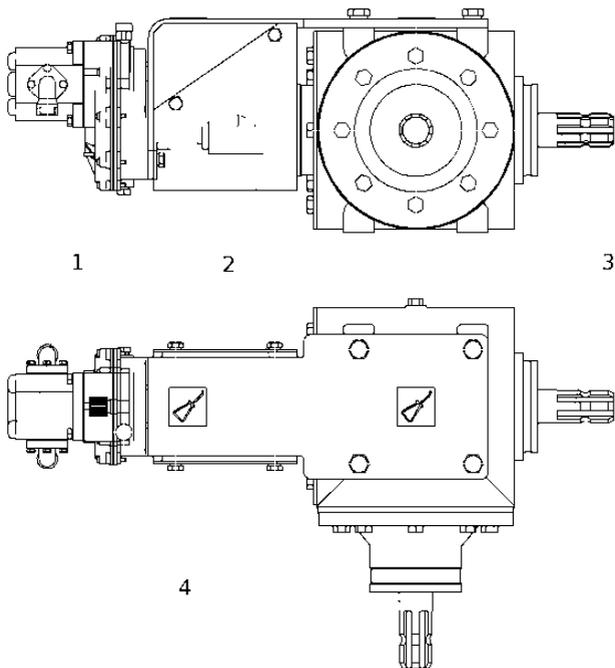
Привод: 1 – мотор-редуктор; 2 – редуктор конический;
